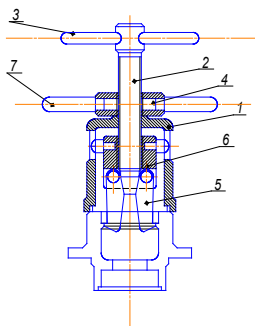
Съемник винтовой для выпрессовки обойм подшипников с помощью захватов
